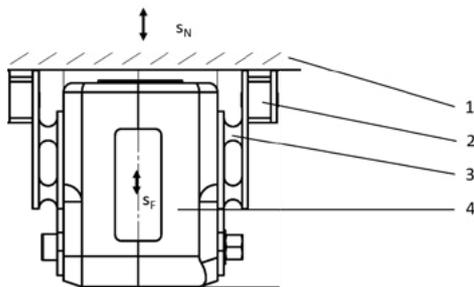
Gerät OSR als Rüttler mit magnetischer Haftbefestigung
